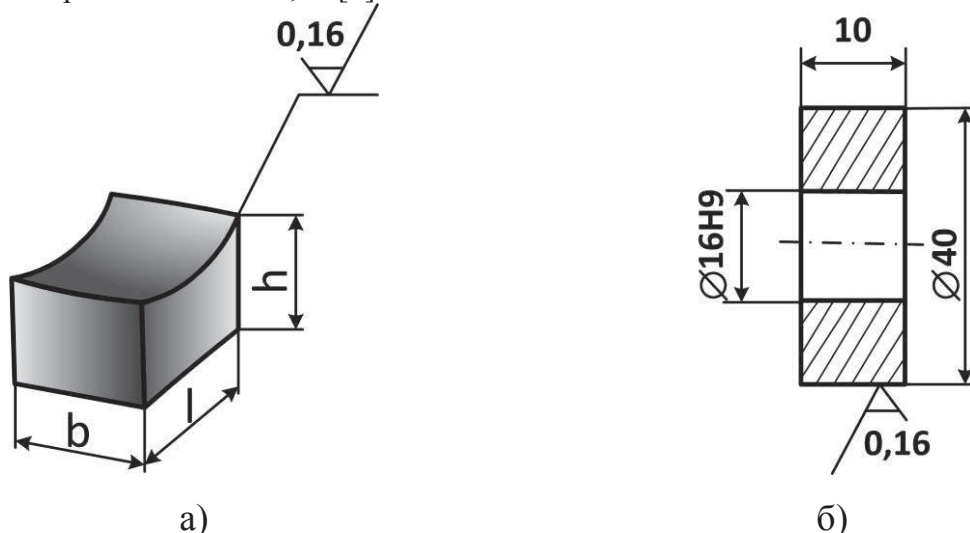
Частичный вкладыш (а) и контртело (б) для проведения испытаний на трение и изнашивание
